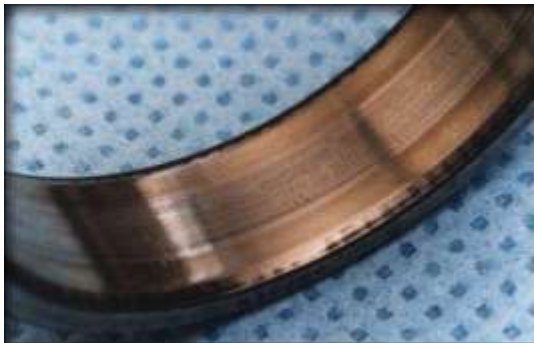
Desgaste abrasivo en cojinetes de motor
